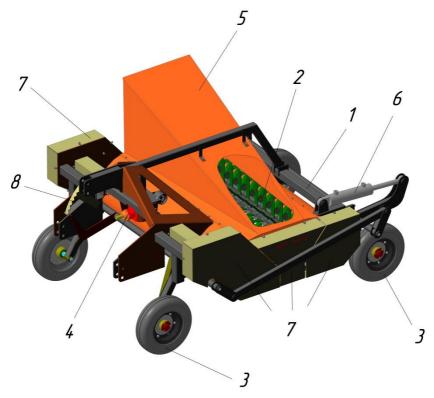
Общий вид машины ботвоуборочной свекловичной МБУ-1,7С 1 — рама; 2 — ротор; 3 — колесо опорное; 4 — привод; 5 — короб отводной; 6 — гидроцилиндр регулировки колес; 7 — ограждения защитные; 8 — линейка.
